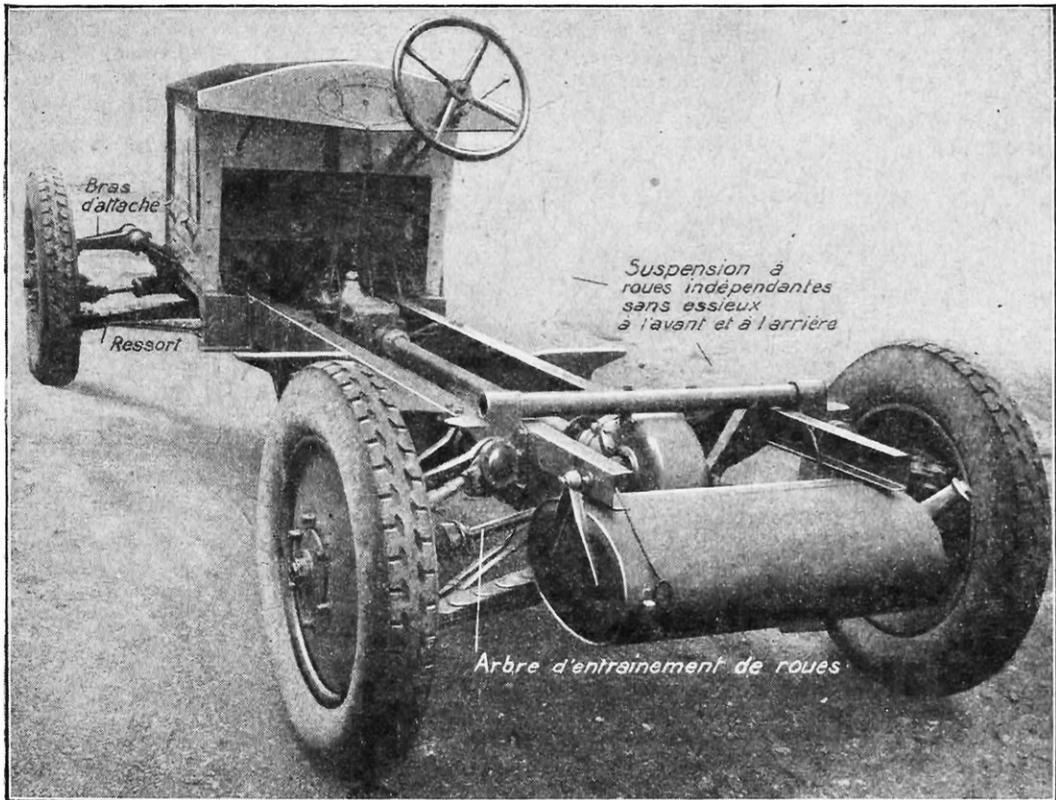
UN CHASSIS A ROUES INDÉPENDANTES
